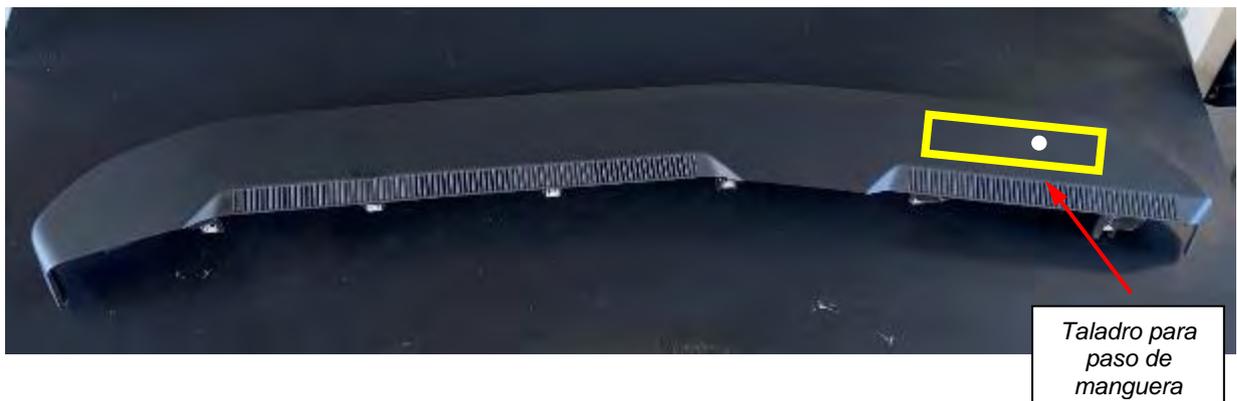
Zona de instalación del taxímetro de salpicadero
